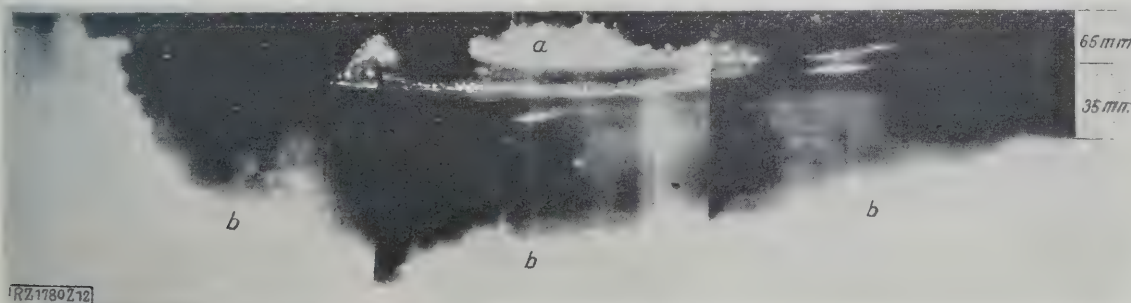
Röntgenaufnahme (positiv) der Warmschweißung des Lokomotivzylinders.
